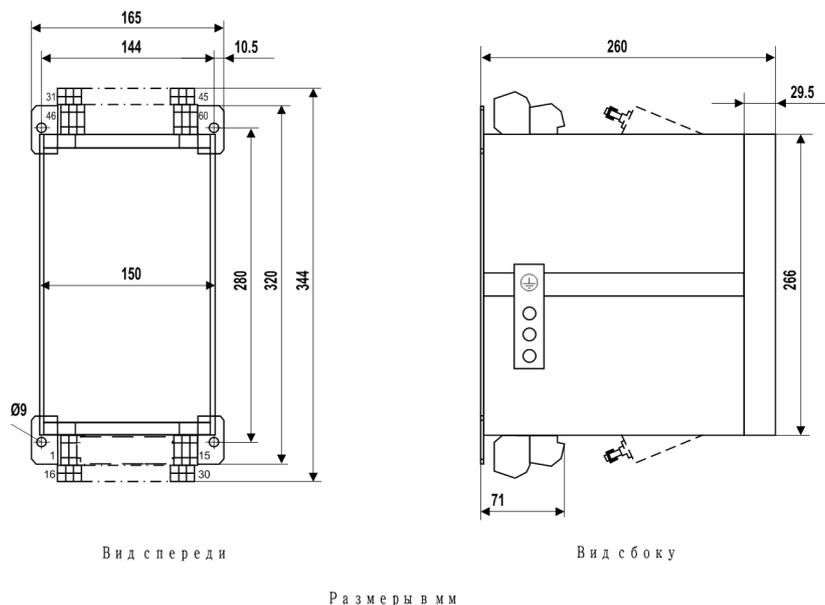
Размерный чертеж устройств 7SJ62 или 7SJ64 для поверхностного монтажа на панели (размер корпуса 1/3)
